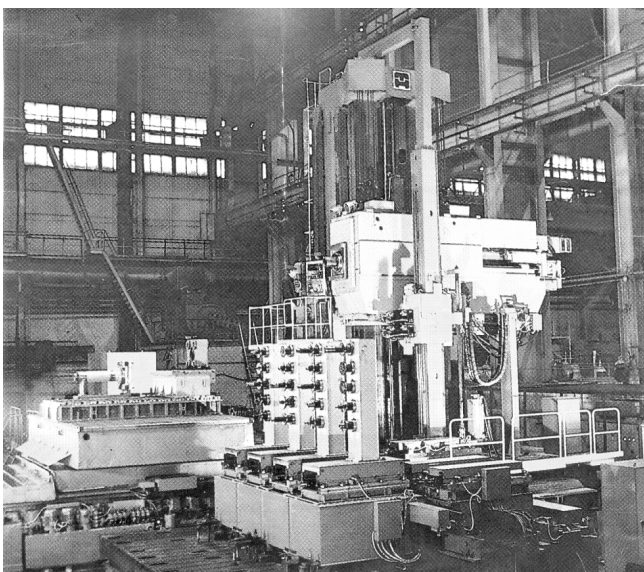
Тяжелый многоцелевой станок сверлильно-фрезерно-расточной группы с поворотным подвижным столом для обработки корпусных деталей массой до 200 т
